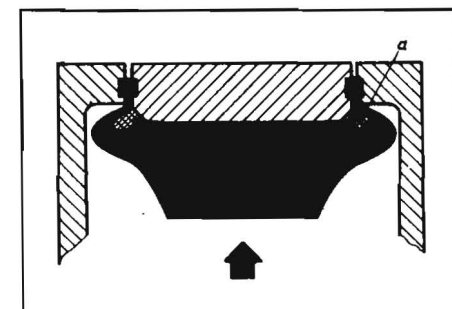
Wirkungsprinzip der Rollkolbenpumpe, drückend;
